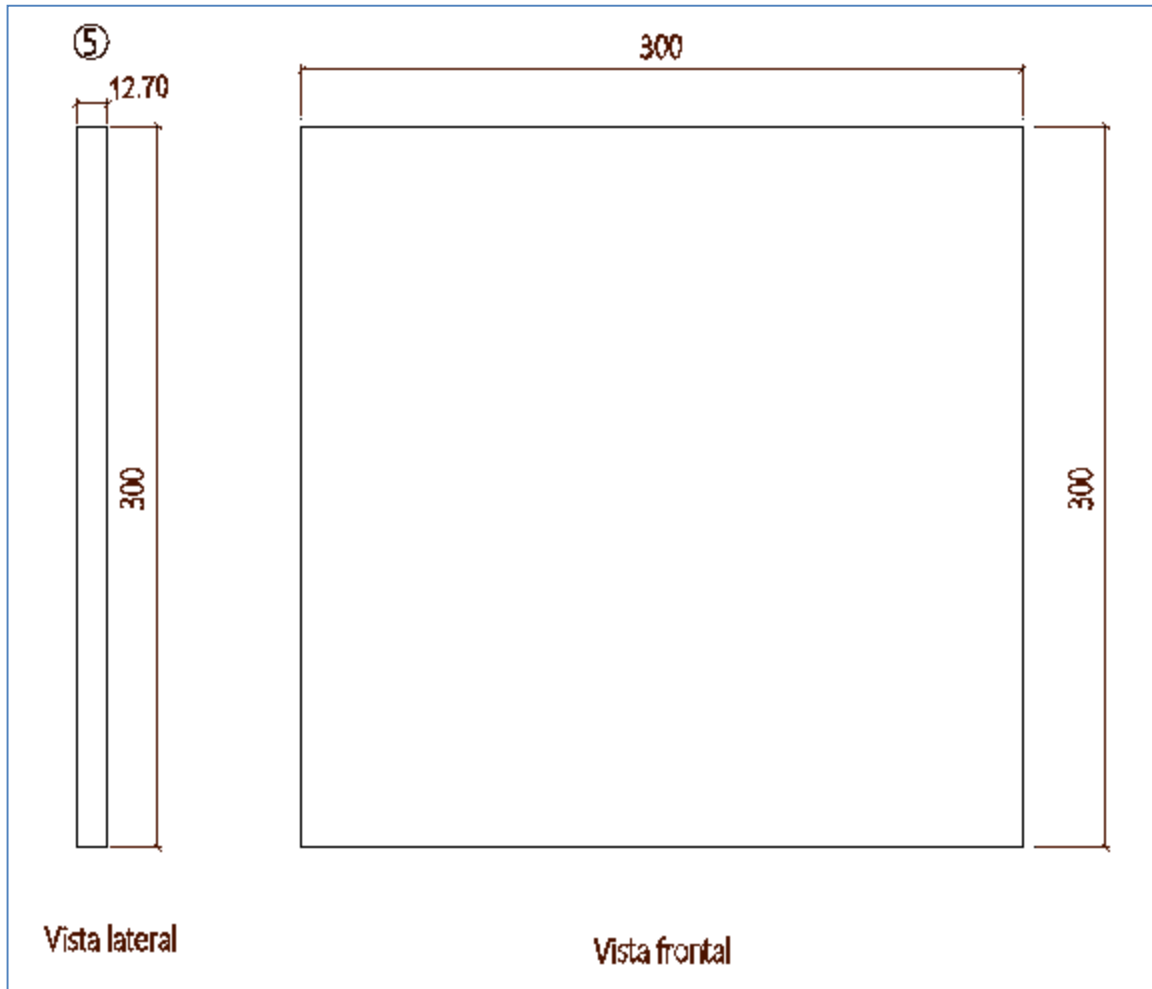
Detalle despiece pieza No.5 modelo 3 tensión.
